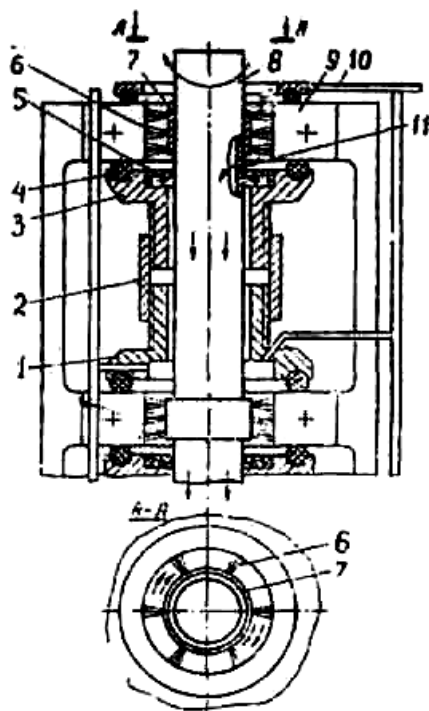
Анодное устройство для восстановления постелей коренных подшипников блока цилиндров двигателя электронатирием:
